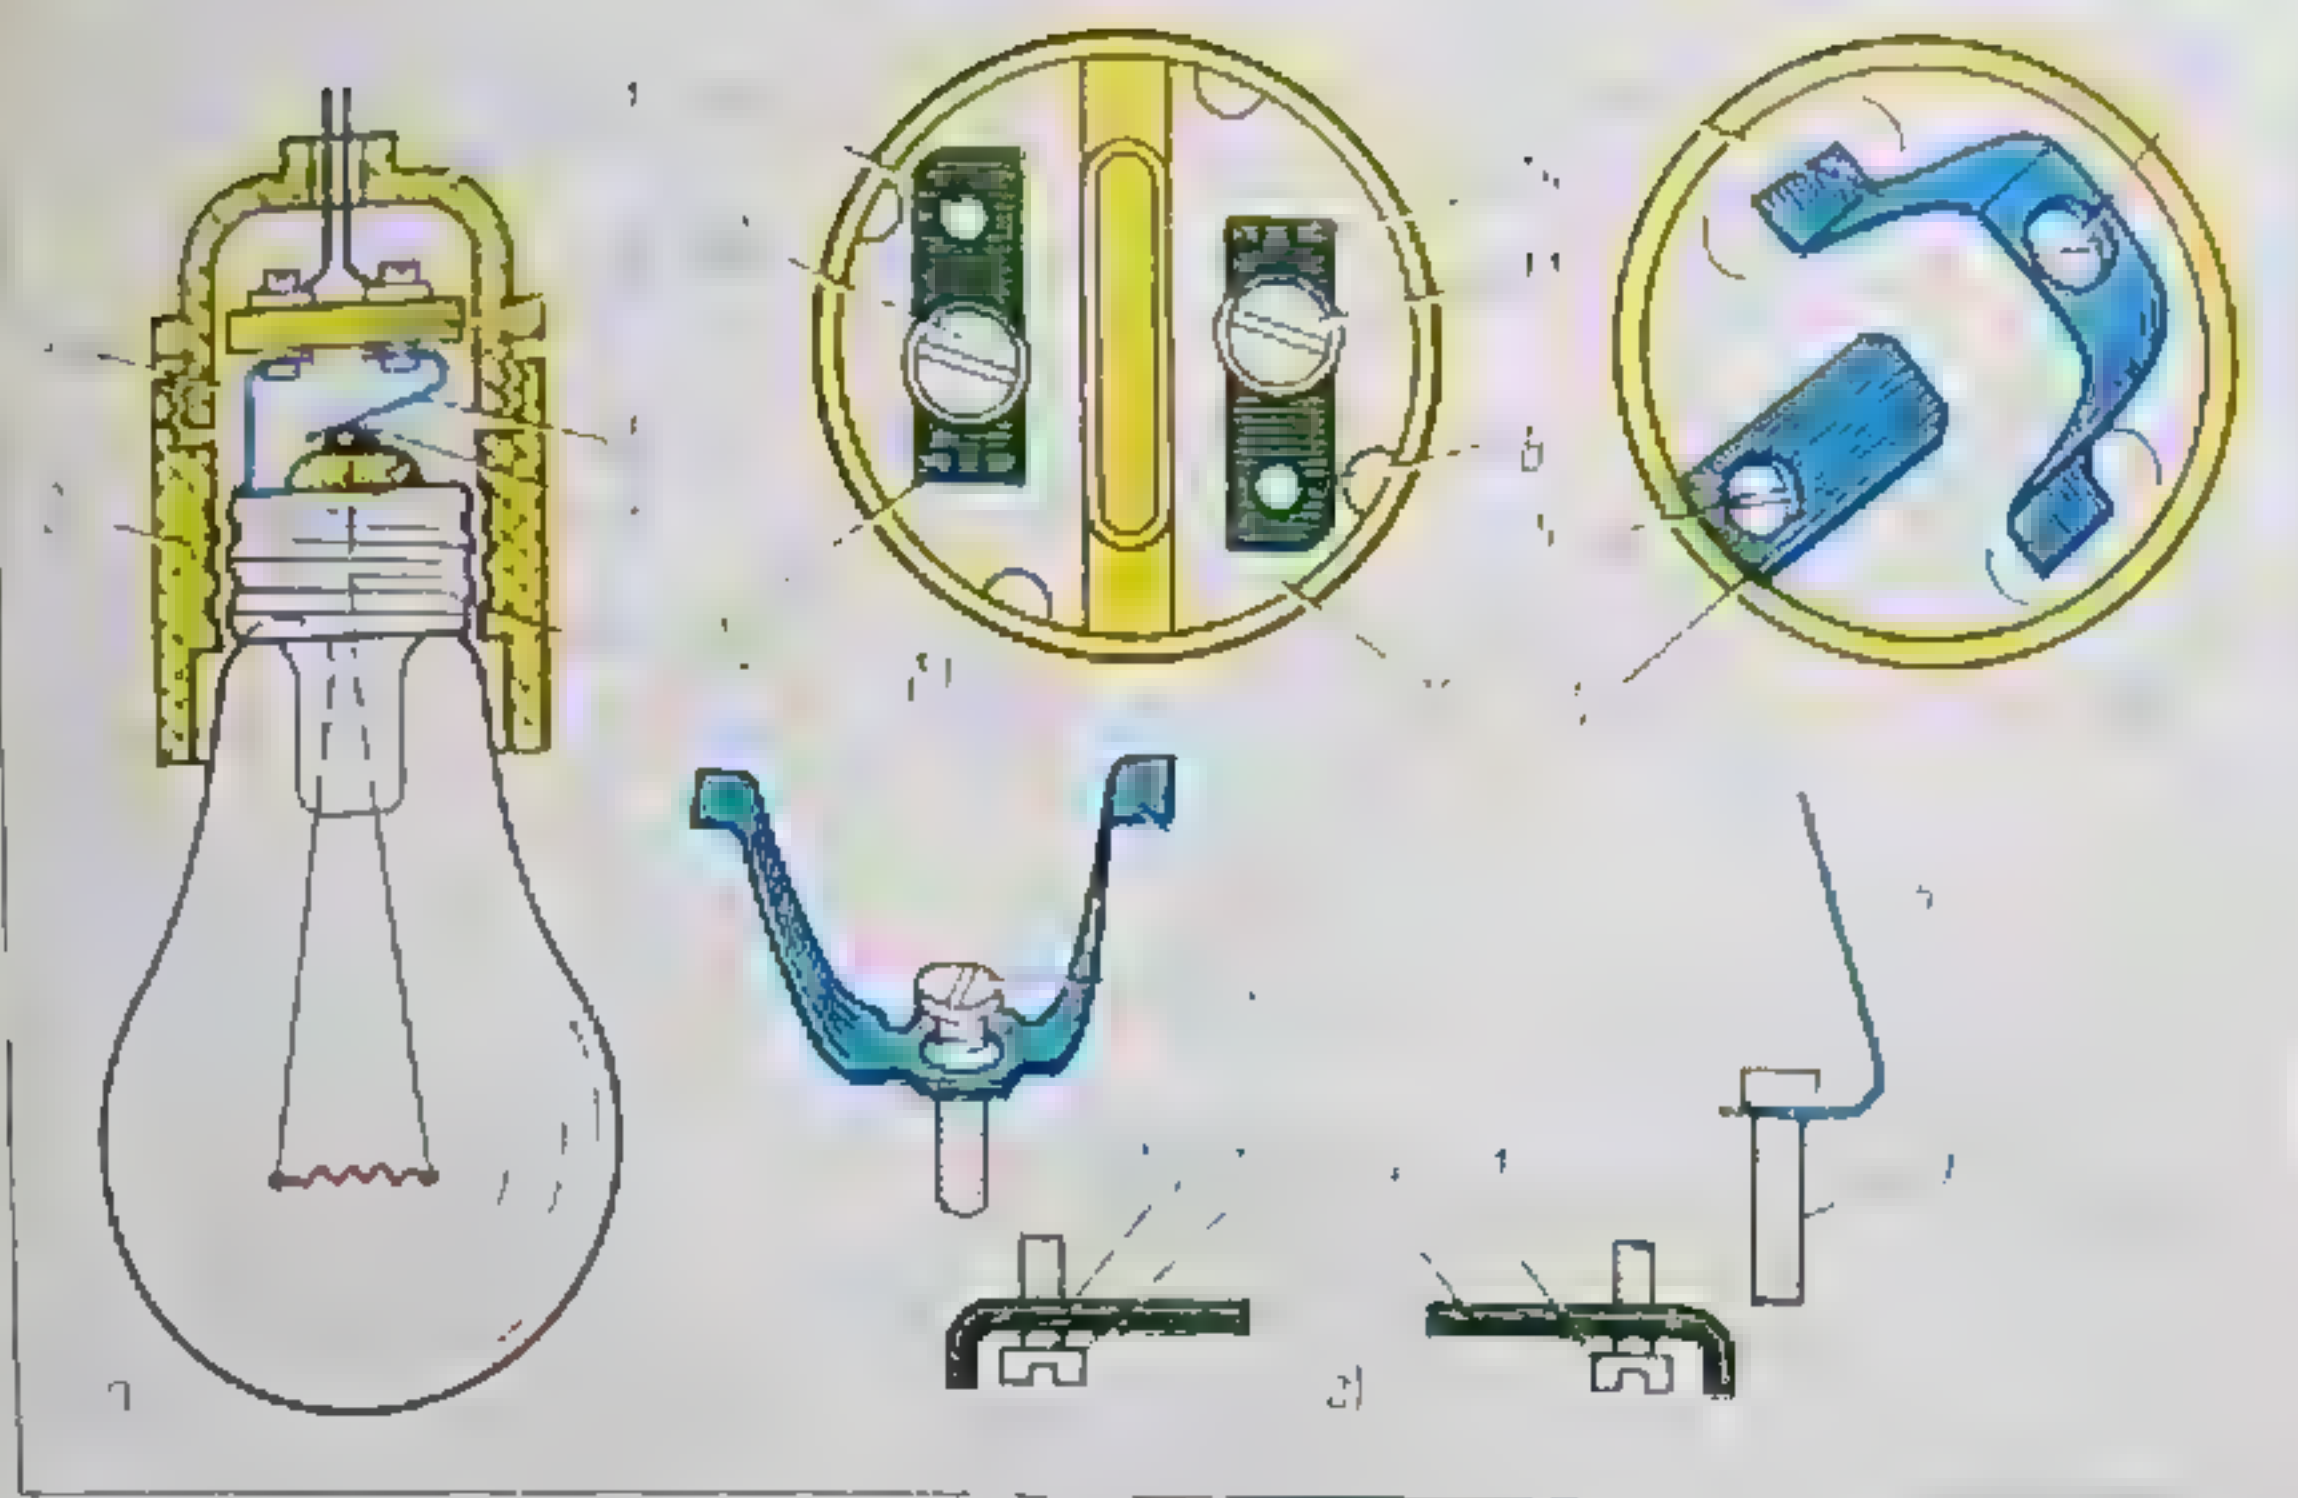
Устройство резьбового патрона для ламп накаливания с цоколем E27
